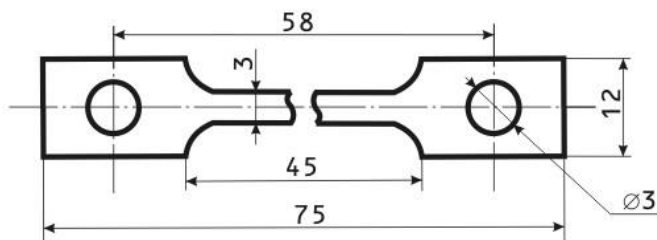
Форма и размеры образца для проведения испытаний на установке ИМАШ-20-75
